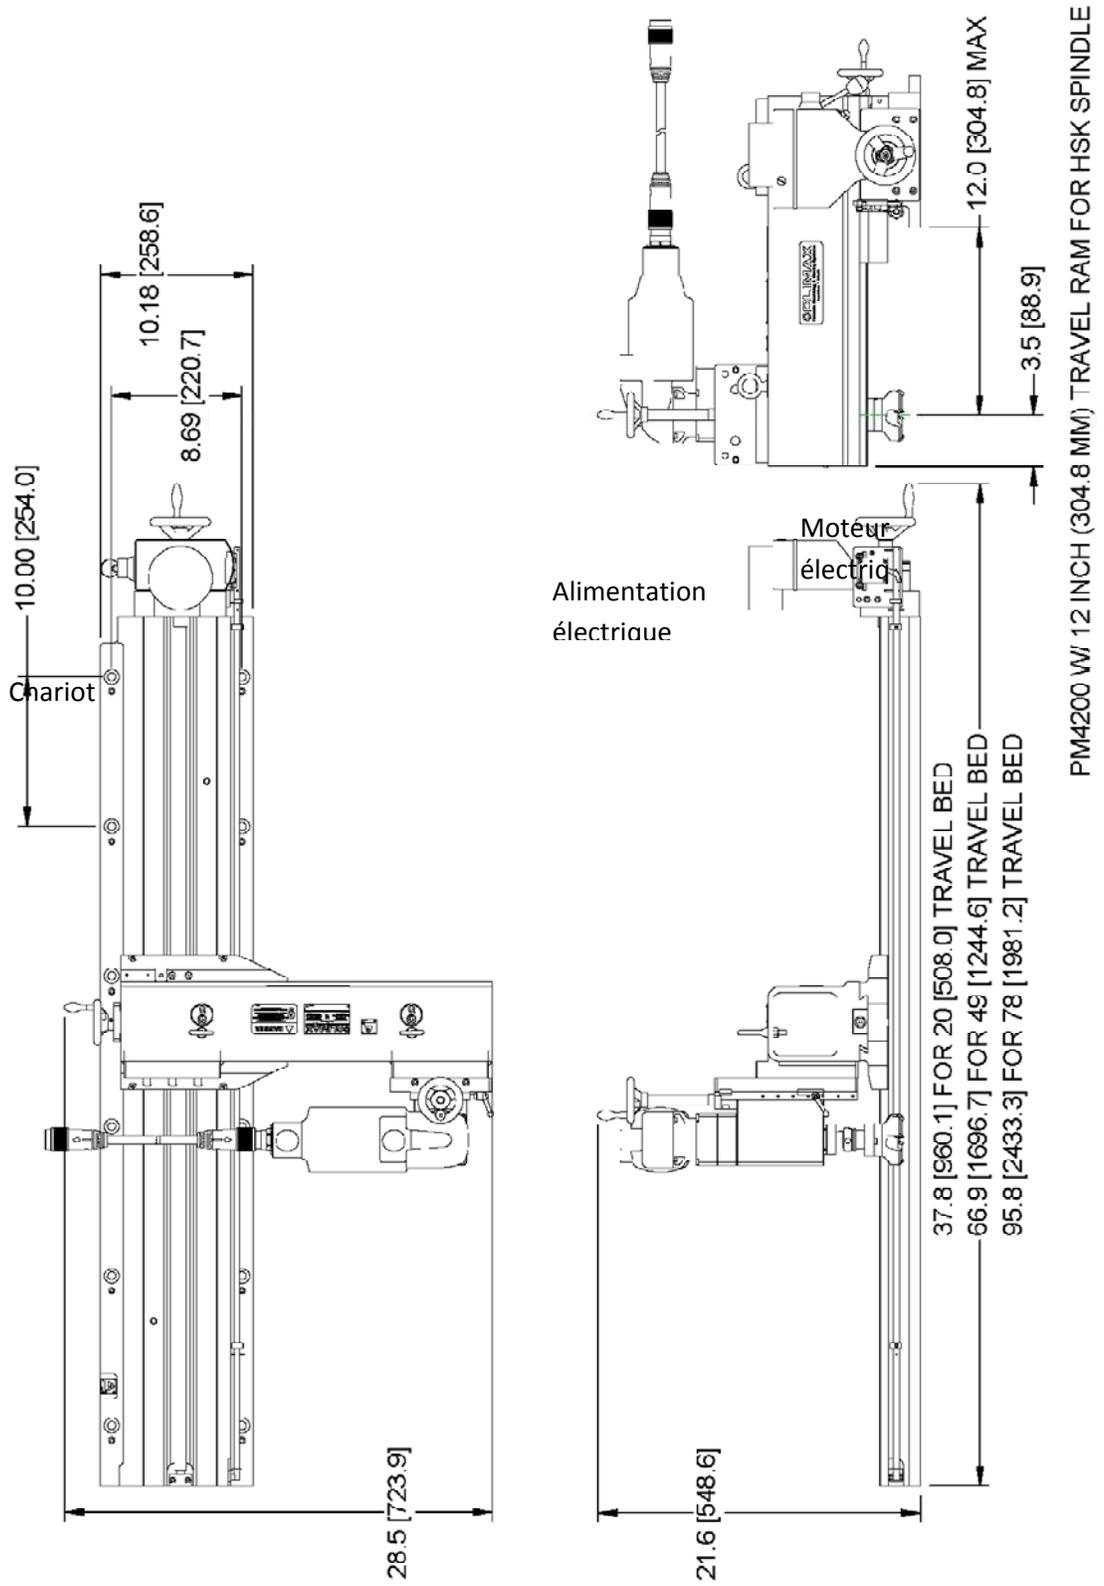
DIMENSIONS POUR LA BROCHE HSK (POUCES ET MILLIMETRES)
